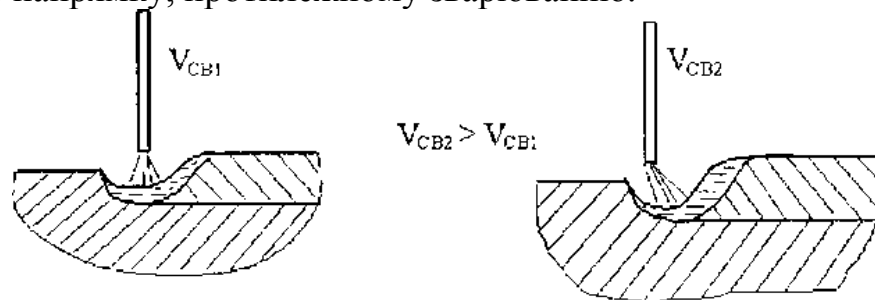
Вплив швидкості зварювання на форму проплавлення
